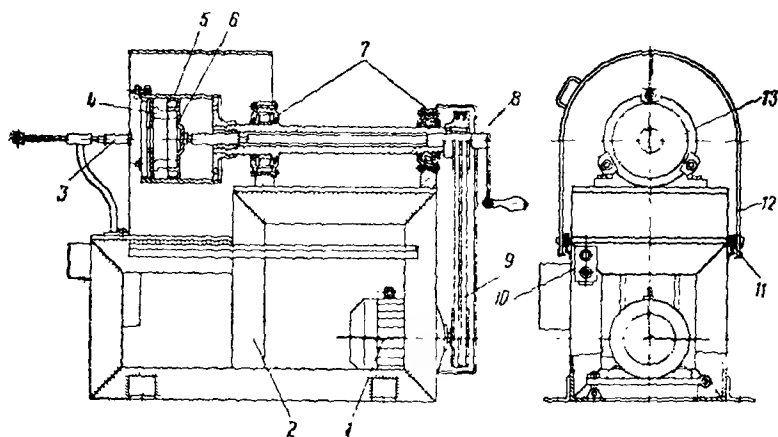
Станок для нанесения пленки эластомера центробежным способом:
